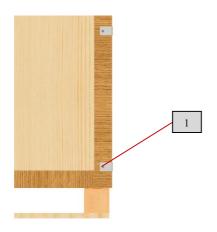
Демонтаж бортов и верхней части упаковки 1- саморез.
